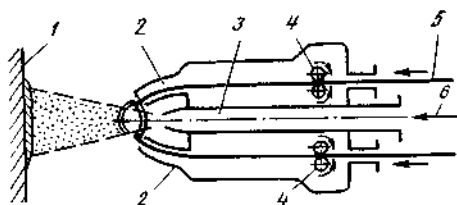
Схема дугового напыления: 1— напыляемая поверхность; 2— направляющие наконечники; 3— воздушное сопло; 4— механизм подачи проволоки; 5— проволока; 6— сжатый воздух
